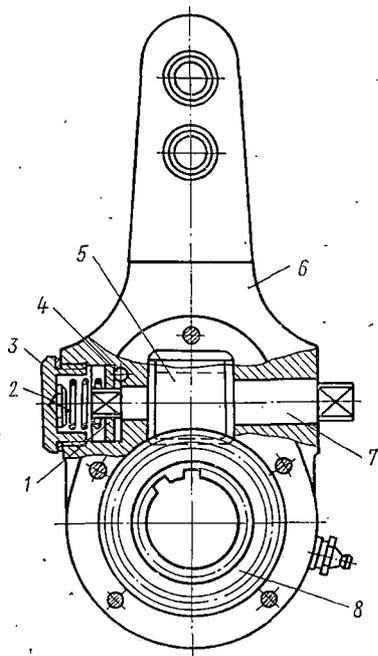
Рычаг привода колодок колесных тормозов с пневматическим приводом:
